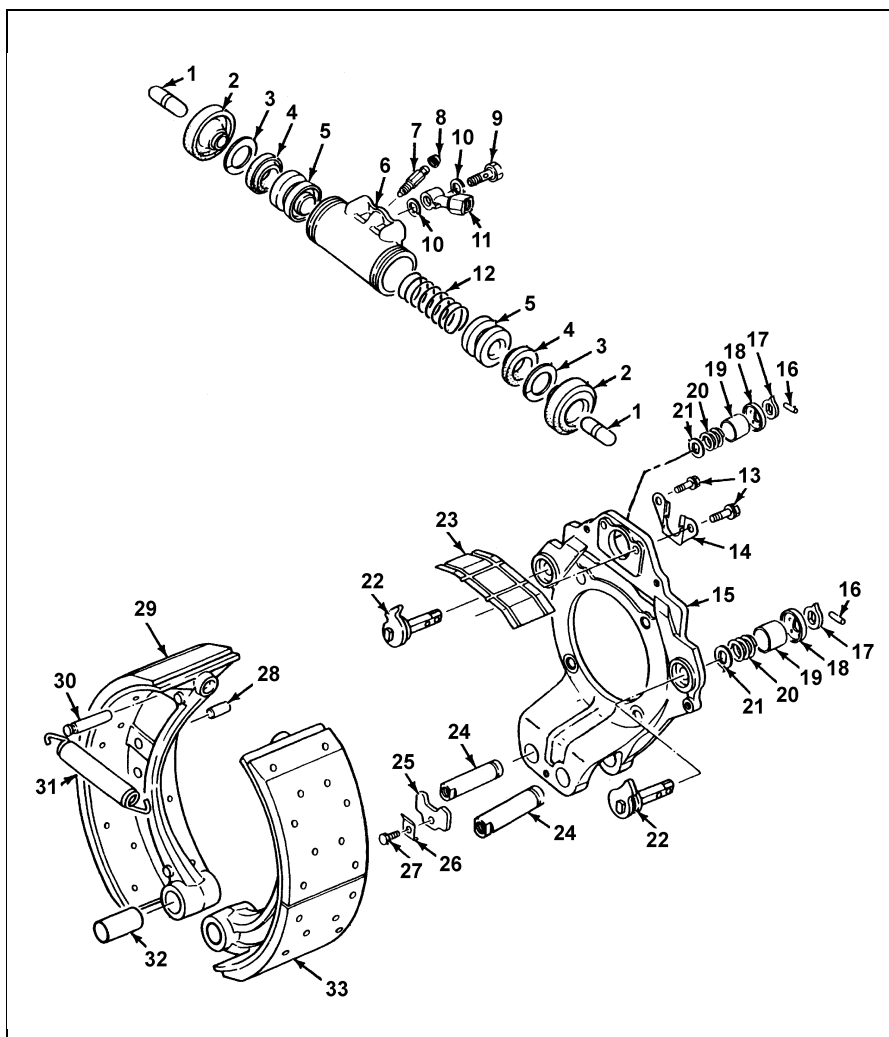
Тормозной механизм. 1 - толкатель, 2 - пыльник, 3 - упорное кольцо, 4 - уплотнительная манжета, 5 - поршень, 6 - корпус рабочего тормозного цилиндра, 7 - штуцер прокачки, 8 - колпачок, 9 - перепускной болт (передние колеса), 10 - медная шайба (передние колеса), 11 - наколочник трубки (передние колеса), 12 - пружина, 13 - болт, 14 - регулировочная пластина, 15 - установочная пластина, 16 - штифт, 17 - индикатор, 18 - крышка чехла, 19 - чехол, 20 - пружина, 21 - шайба, 22 - регулировочный кулачок, 23 - кожух рабочего тормозного цилиндра, 24 - анкерный палец, 25 - стопорная пластина, 26 - фиксатор болта, 27 - болт, 28 - направляющий штифт, 29 - тормозная колодка, 30 - палец возвратной пружины, 31 - возвратная пружина в сборе, 32 - втулка, 33 - тормозная колодка.
